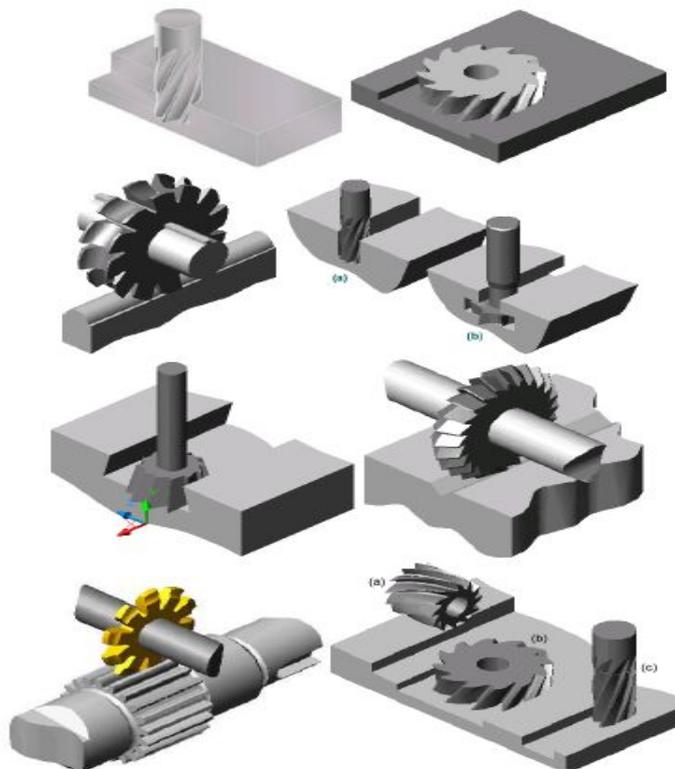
Vários exemplos de maquinagem em fresadoras. Fonte - IPB
